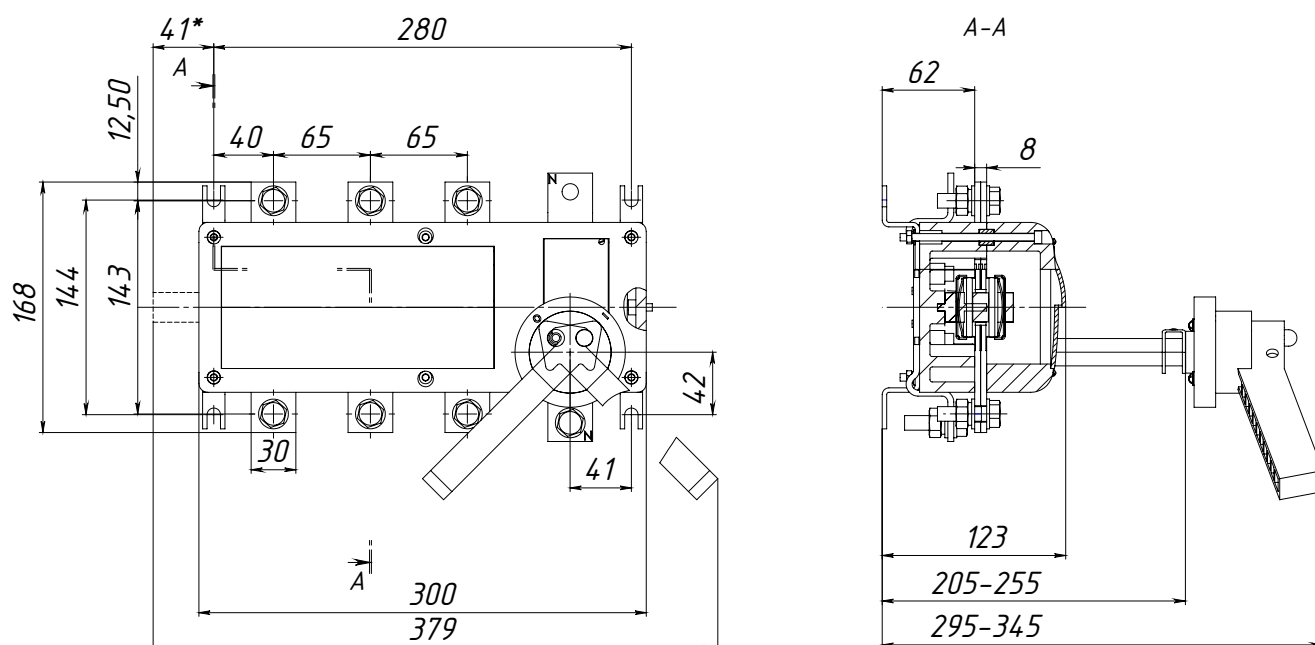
Выключатель-разъединитель ВНК-37-31130-32 УХЛ3
